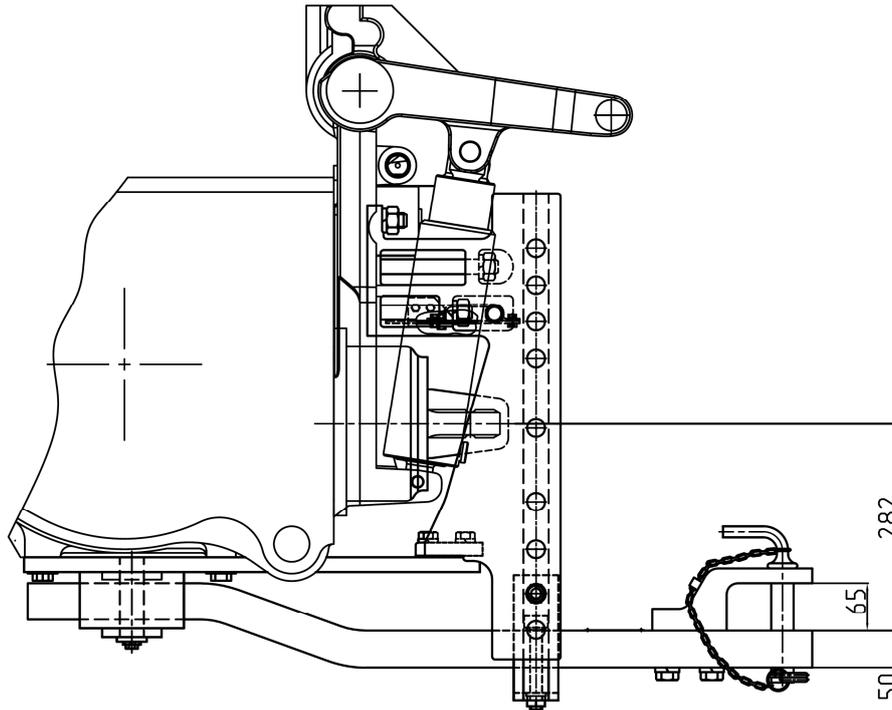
Schéma des variantes d'installation du dispositif TSU-1M-01 (barre de traction)
